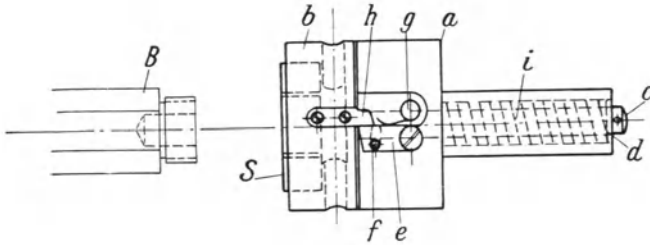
Gewindeschneid-Vorrichtung für Automaten.
